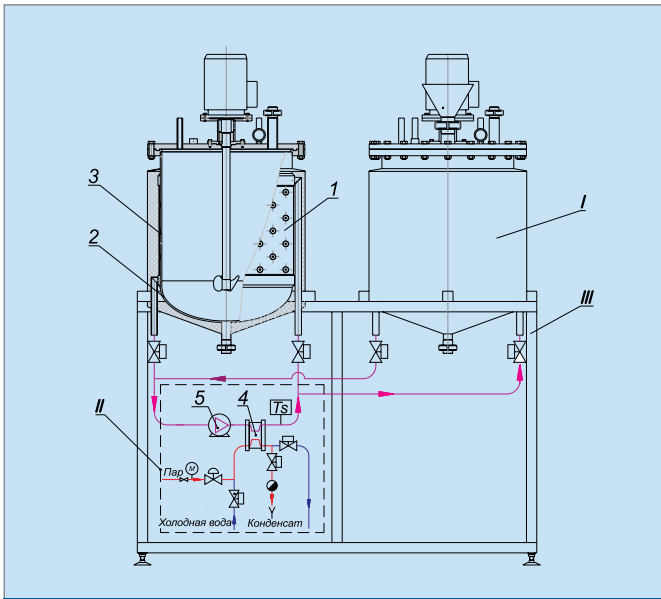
Схема ферментатора и системы подачи теплоносителя: 1 – ферментатор; II – блок ГВС; III – площадка опорная; 1 – универсальная рубашка; 2 – эллиптическое дно; 3 – кислотостойкое покрытие (напыление); 4 – теплообменник; 5 – специальный центробежный насос
